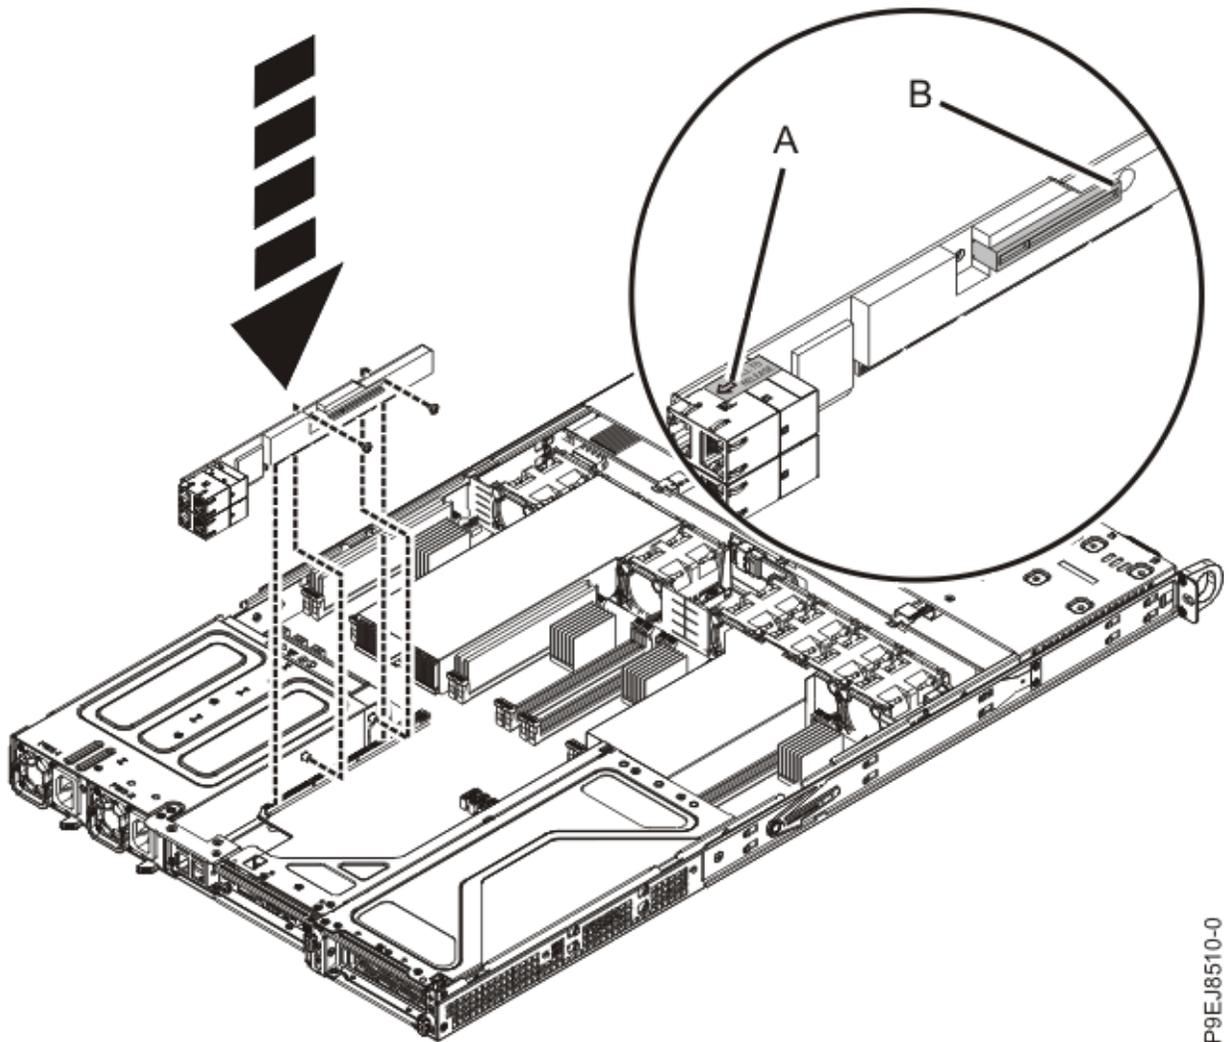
Schrauben der PCIe-Adapterriserkarte austauschen
